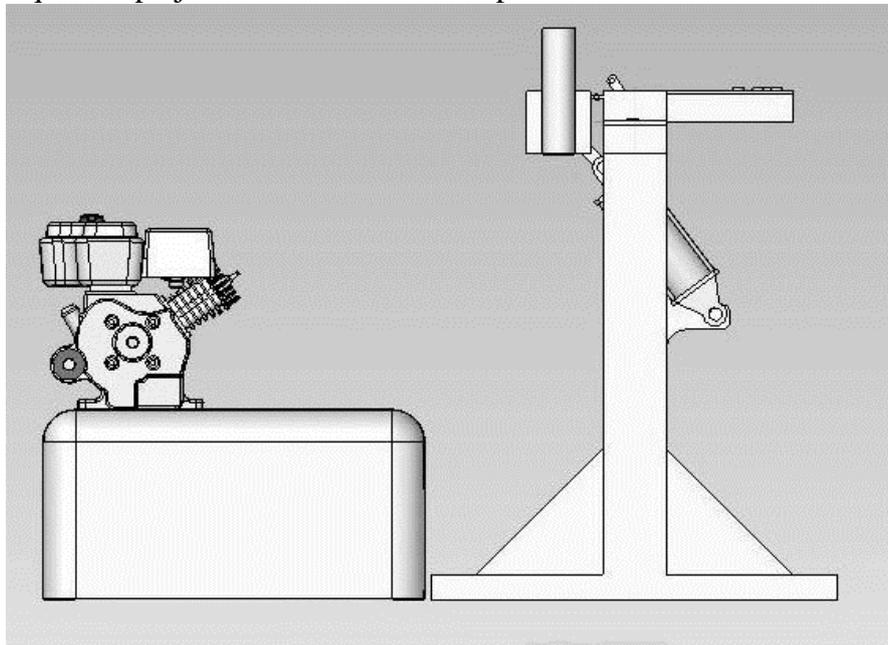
Montagem do sistema hidráulico, vista isométrica
